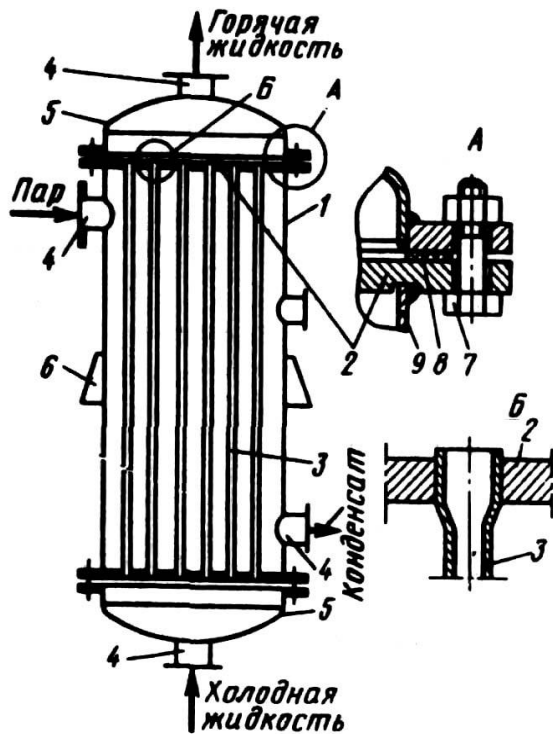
Схема вертикального одно-ходового кожухотрубчатого теплообменника с неподвижными трубными решетками и размещение труб в трубной решетке: 1 – корпус; 2 – трубная решетка; 3 – греющая труба; 4 – патрубок; 5 – днища; 6 – опорная лапа; 7 – болт; 8 – прокладка; 9 – обечайка
